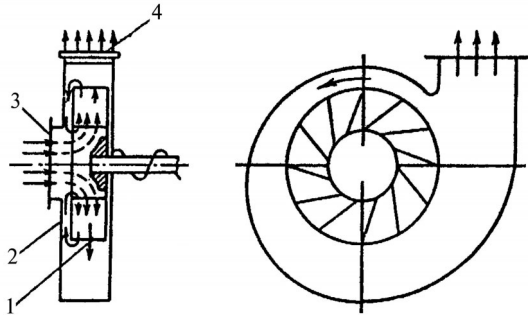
Аеродинамічна схема відцентрового вентилятора: 1 - робоче колесо; 2 - корпус (кожух); 3 - вхідний патрубок; 4 - вихідний патрубок.
